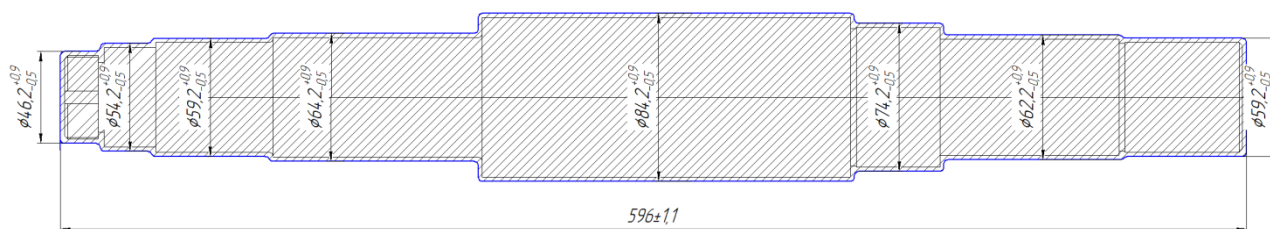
Ескіз заготовки штамповка деталі «Вал черв'ячного редуктора»
